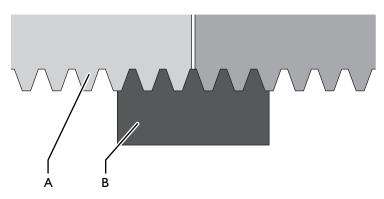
Montagehilfe für Zahnstangenmontage
